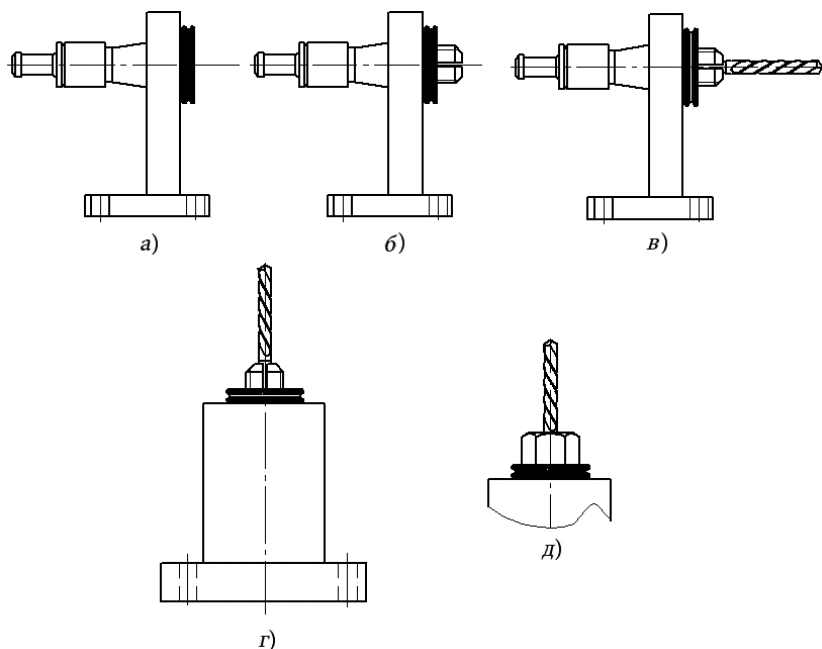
Последовательность сборки оправки с осевым инструментом (сверлом):
